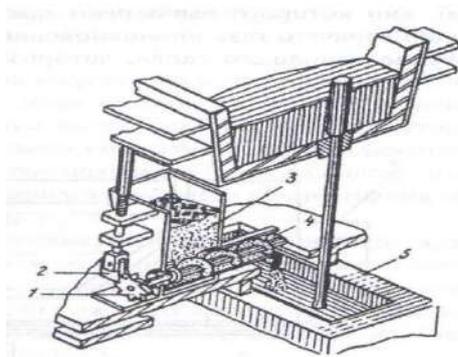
Устройство для механической подачи защитной смеси в кристаллизатор [5, 6]: 1 – храповое колесо; 2 – исполнительный механизм; 3 – бункер со смесью; 4 – вал шнека; 5 - кристаллизатор
